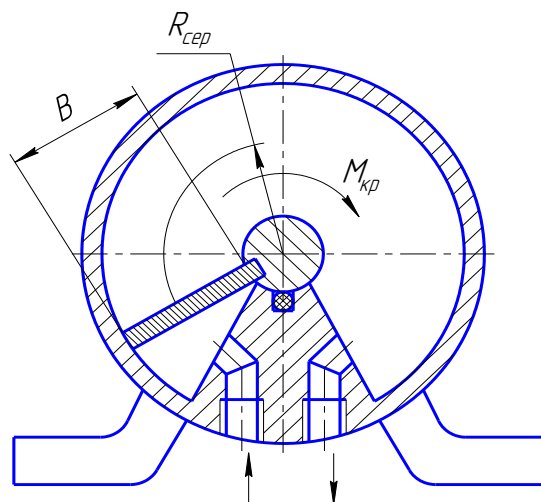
Лопатевий неповноповоротний пневмопривід
